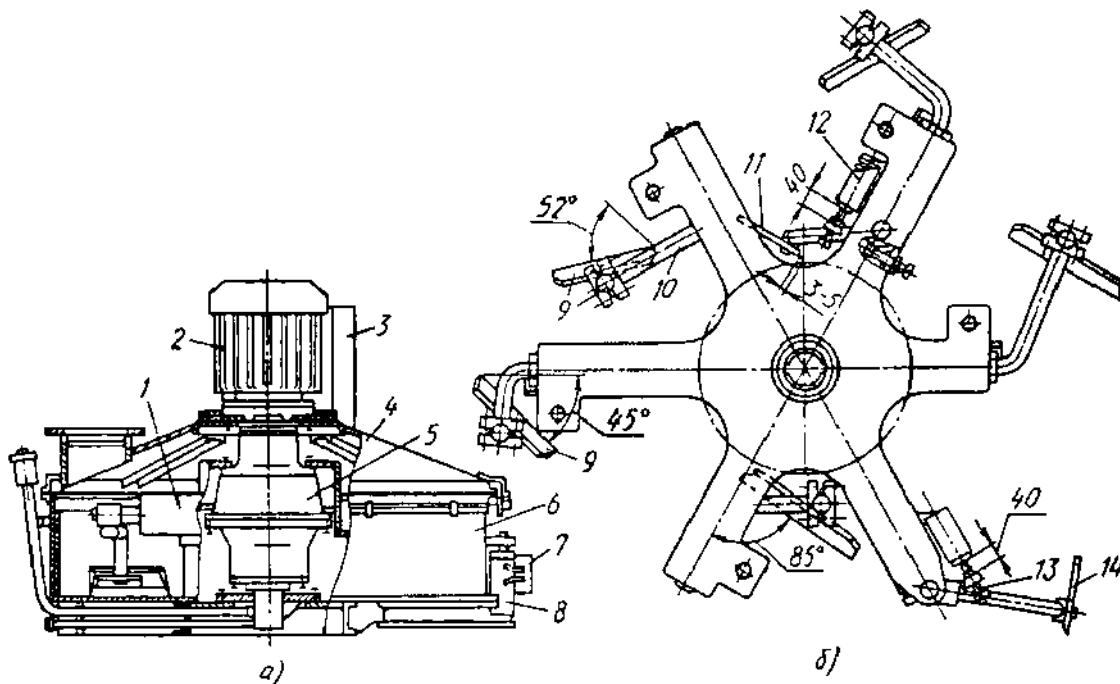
Роторный смеситель с вертикальным валом: *а* - общий вид; *б* - лопастной аппарат; 1 - лопастной аппарат; 2 - электродвигатель; 3 - пульт управления; 4 - крышка чаши; 5 - редуктор; 6 - неподвижный корпус - чаша; 7 - пневмоцилиндр затвора; 8 - затвор; 9 - держатель лопасти; 10 - водило; 11 - лопасть для очистки обечайки внутреннего стакана; 12 - амортизатор; 13 - регулировочный винт; 14 - лопасть для очистки стенок корпуса
